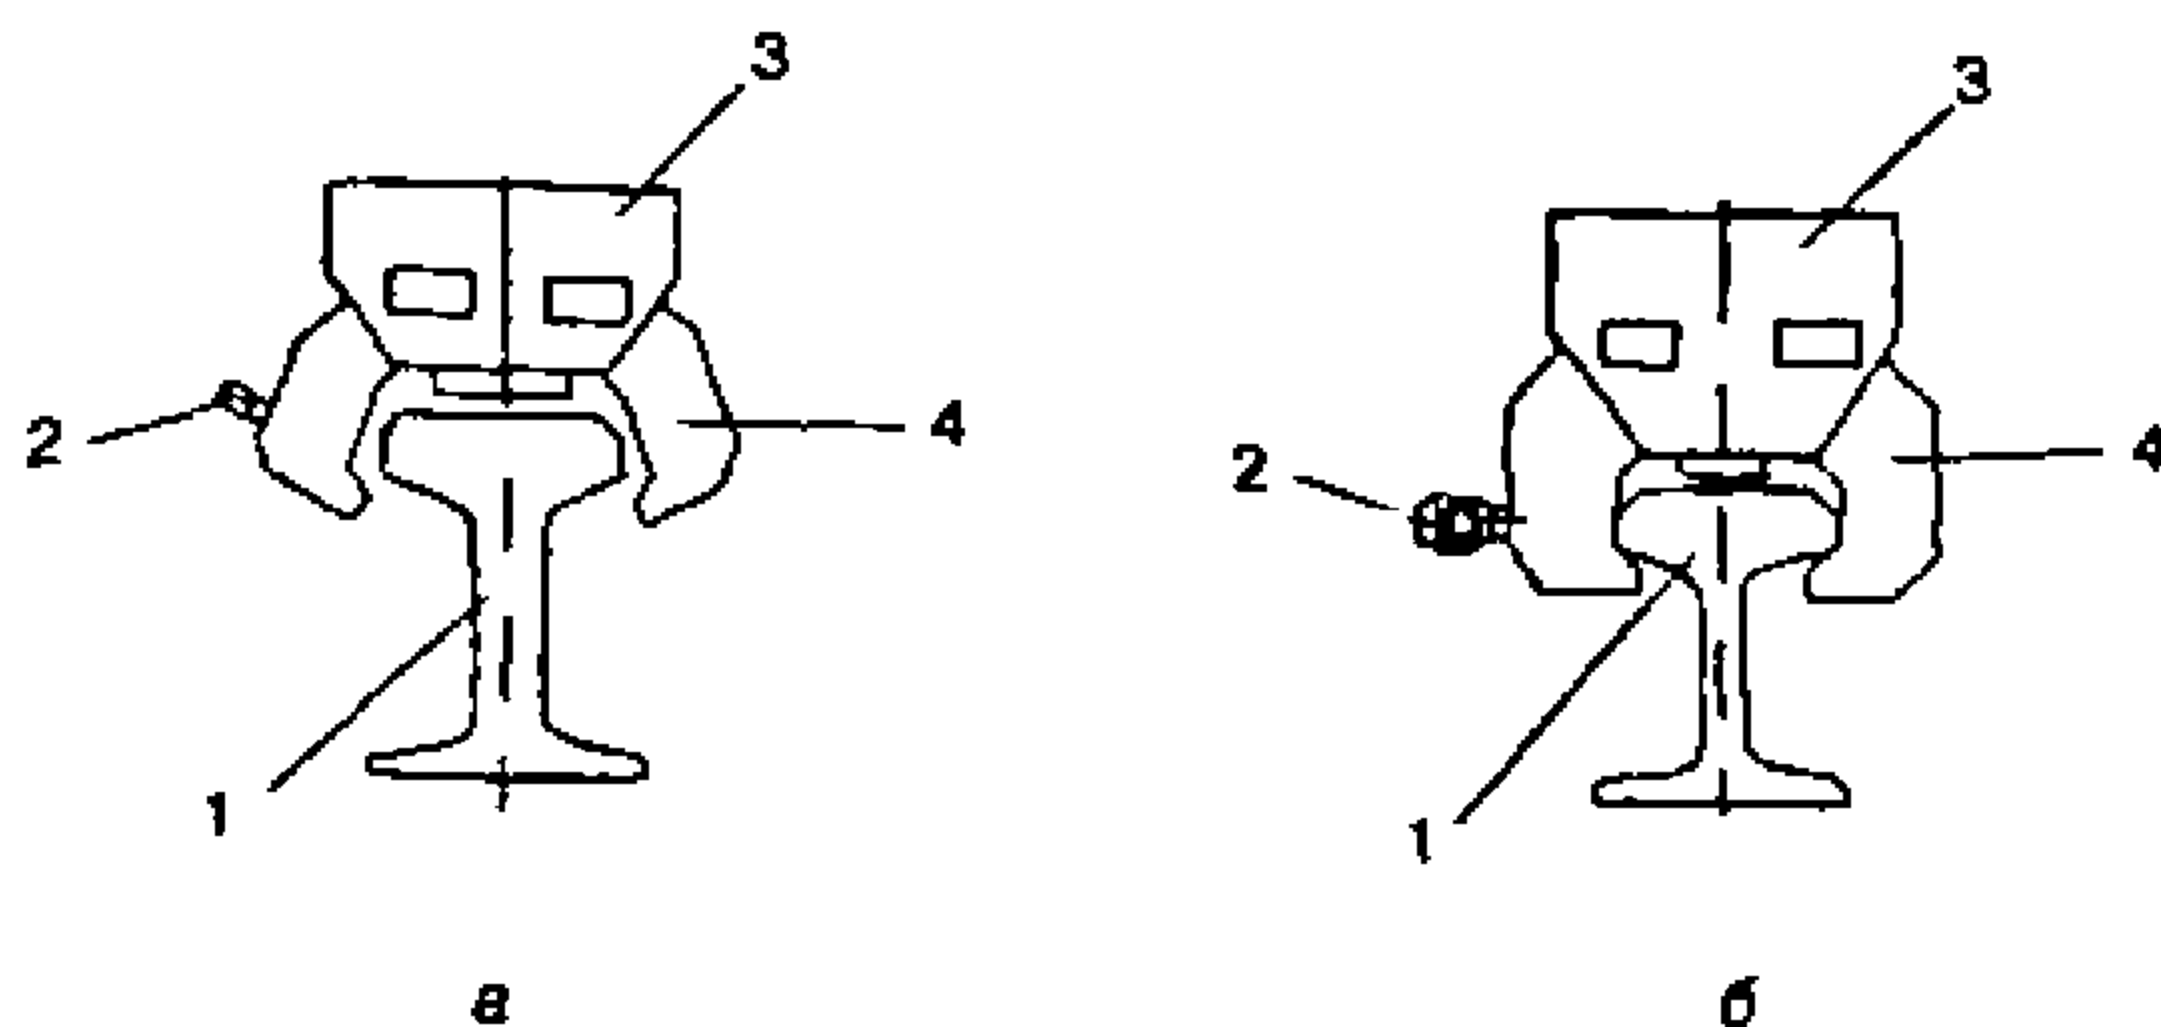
Рельсовый противоугонный захват с ручным приводом:
